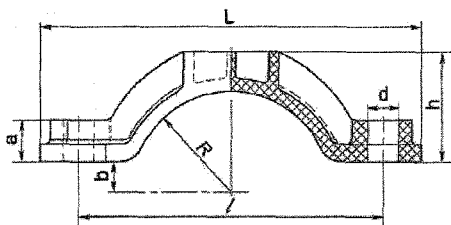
Внешний вид и габаритные размеры крепления ВКК
